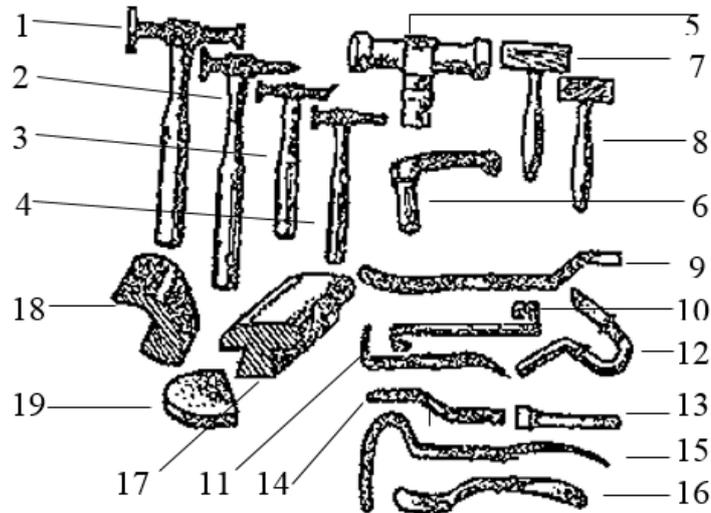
Ручной инструмент для правки и рихтовки кузова:
